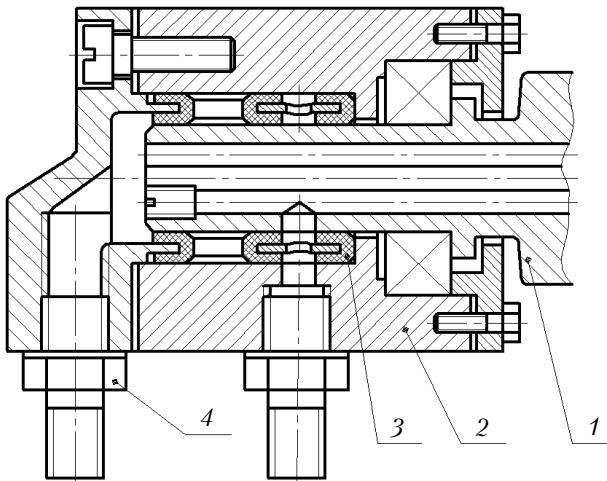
Муфта для подачи сжатого воздуха во вращающийся пневмоцилиндр
